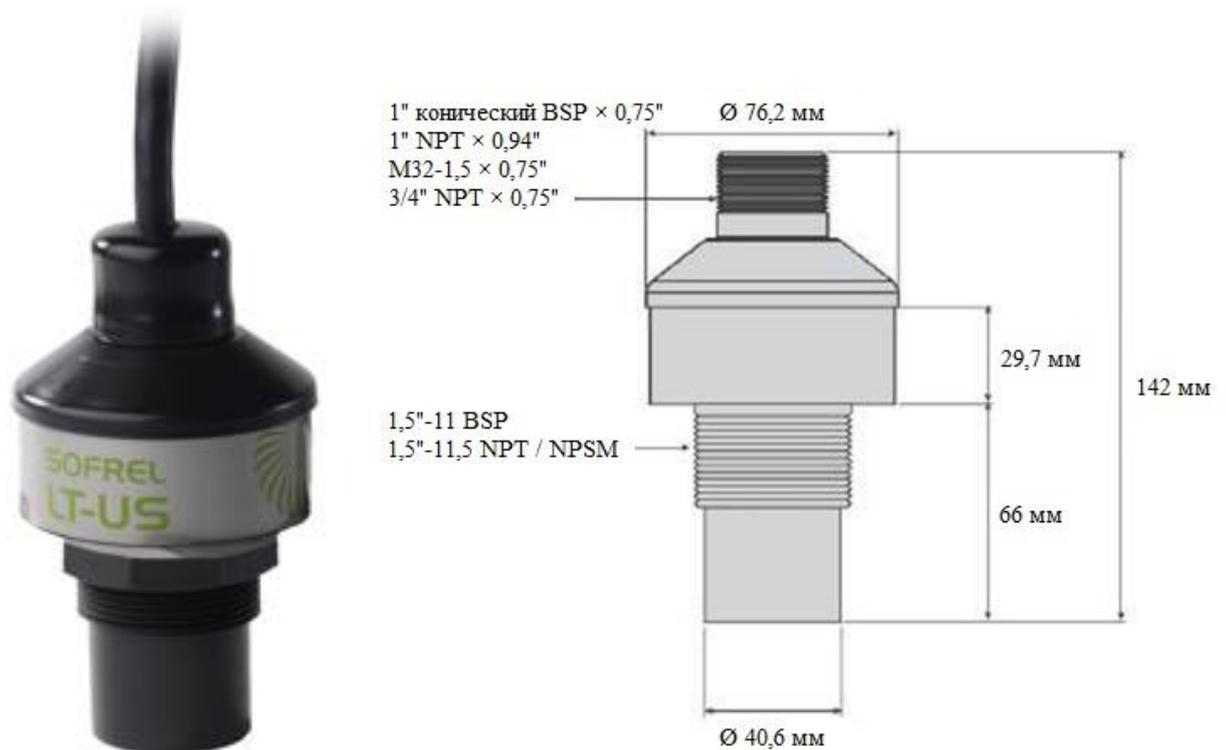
Внешний вид и габаритные размеры акустического преобразователя
